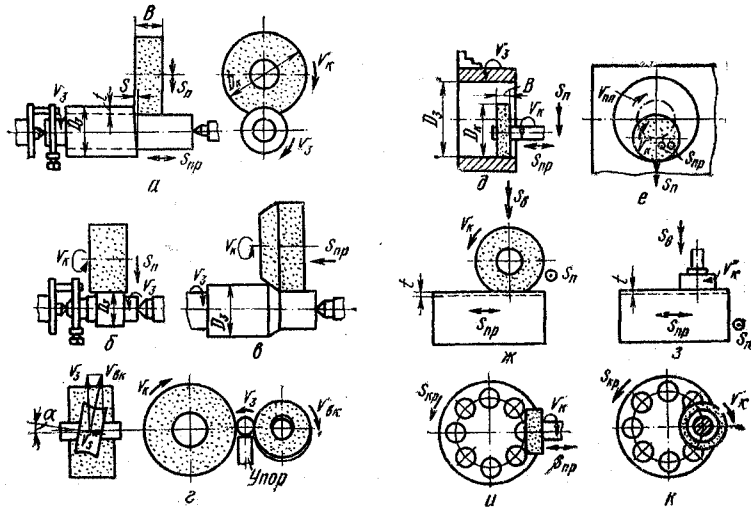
Схемы шлифования поверхностей заготовок на шлифовальных станках
